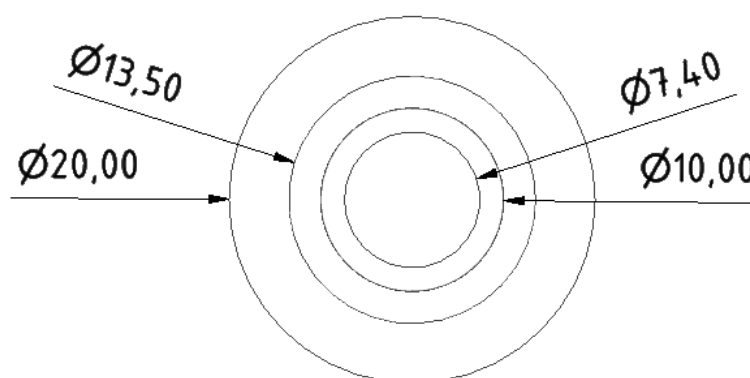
Hřídel pasivního kloubu - pohled z horní strany.
